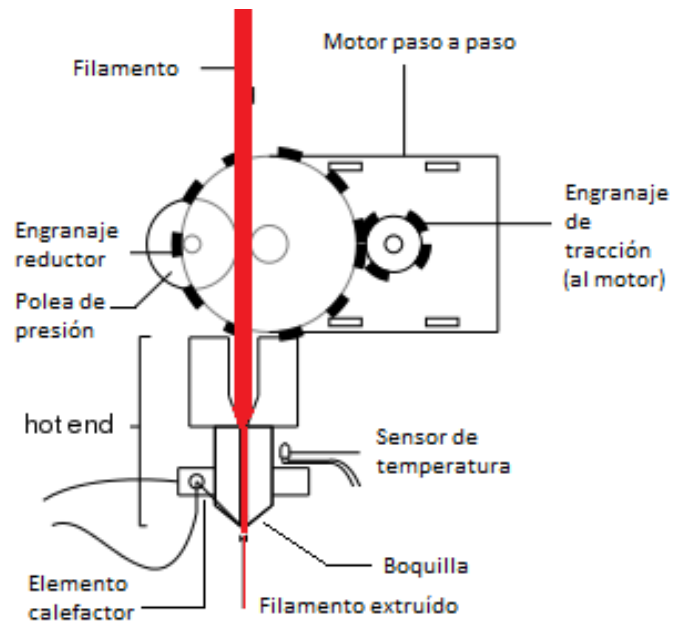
Extrusor de rodillo de impresoras 3D.
